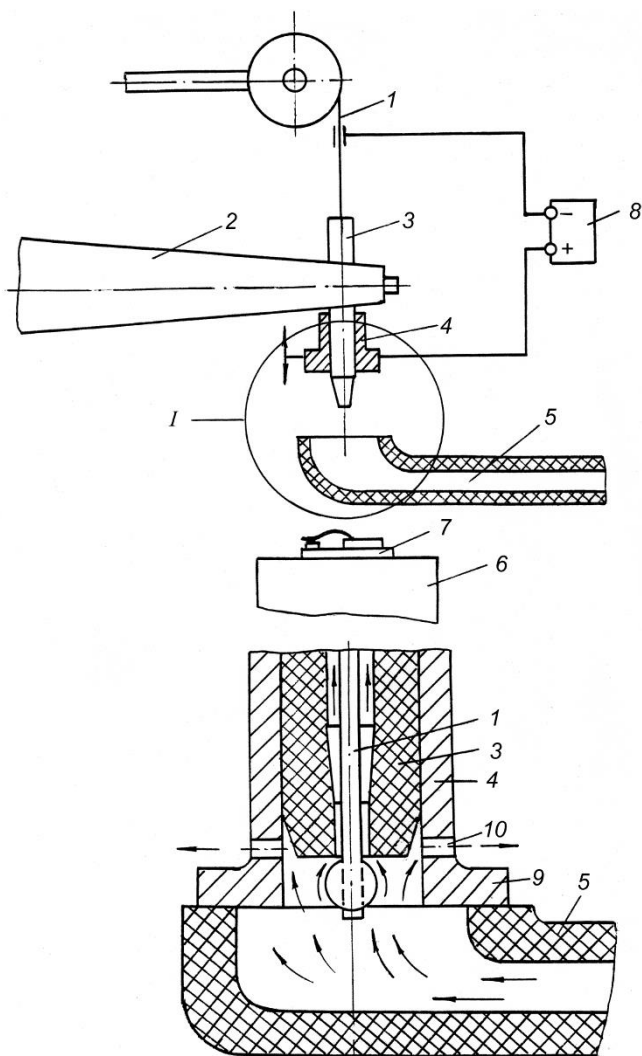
Устройство для формирования шарика оплавлением проволоки: а – схема устройства; б – фрагмент устройства в момент образования шарика: 1 – проволока; 2 – сварочная головка; 3 – микросварочный инструмент; 4 – трубчатый электрод; 5 – трубопровод; 6 – столик; 7 – подложка; 8 – источник питания; 9 – электрод с выступом; 10 – отверстия в стенке электрода
